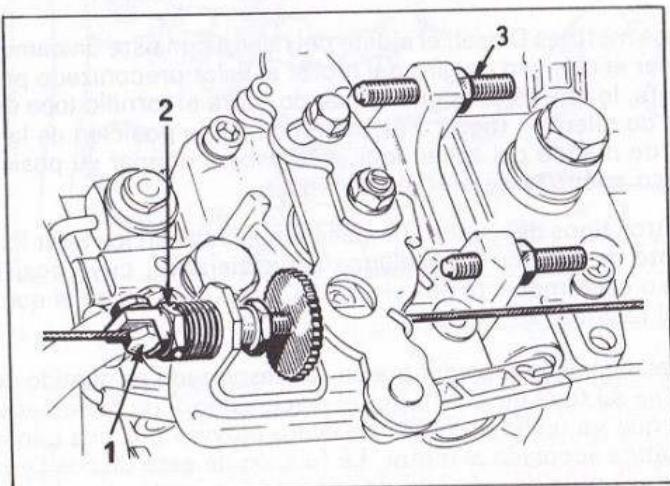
Dispositivo de arranque en frío para los motores Diesel.
